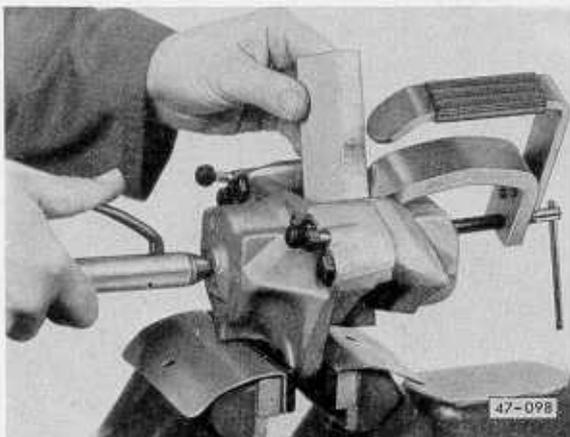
Kolben mit Druckluft aus dem Zylinder drücken.
